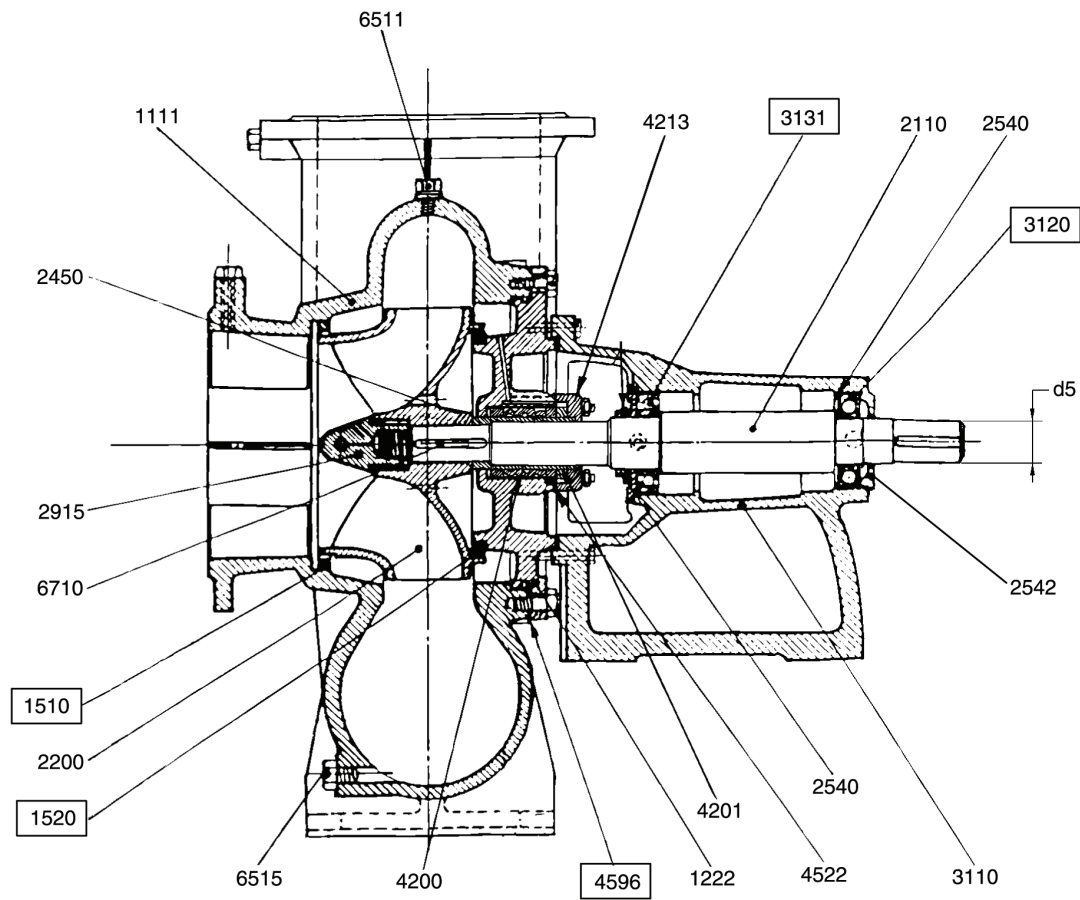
Plano seccionado, NK 200-500, 250-400, 250-500 "sobredimensionadas"
